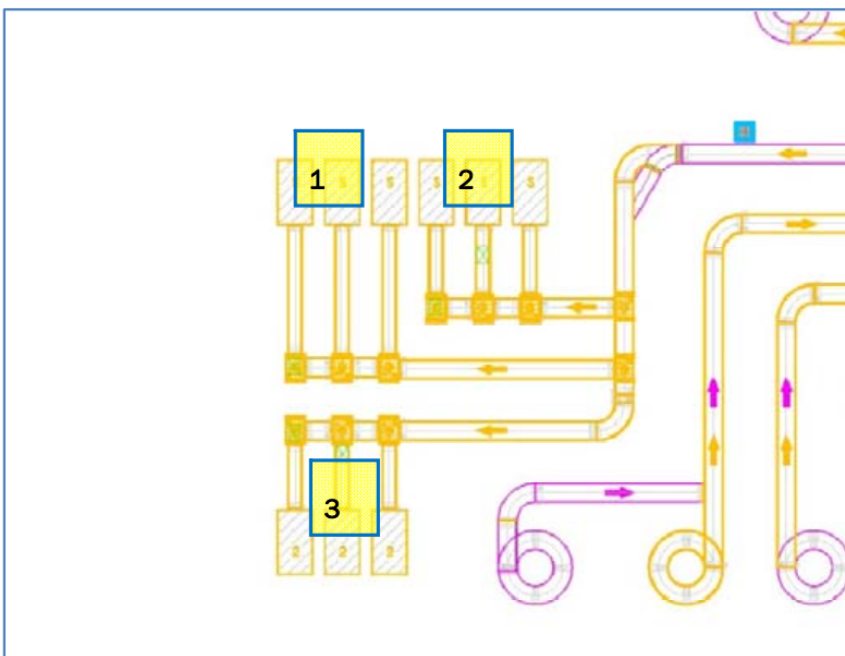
Detalle secuenciador escenario automático Fuente Elaboración propia
